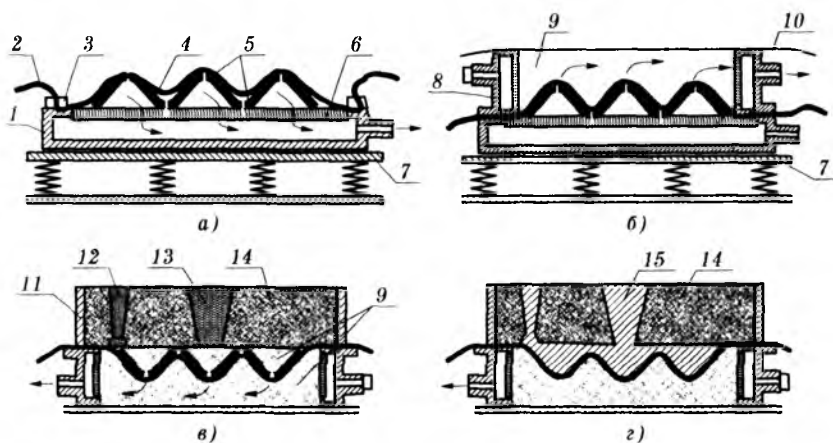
Изготовление литейной формы методом вакуумно-плёночной формовки:
